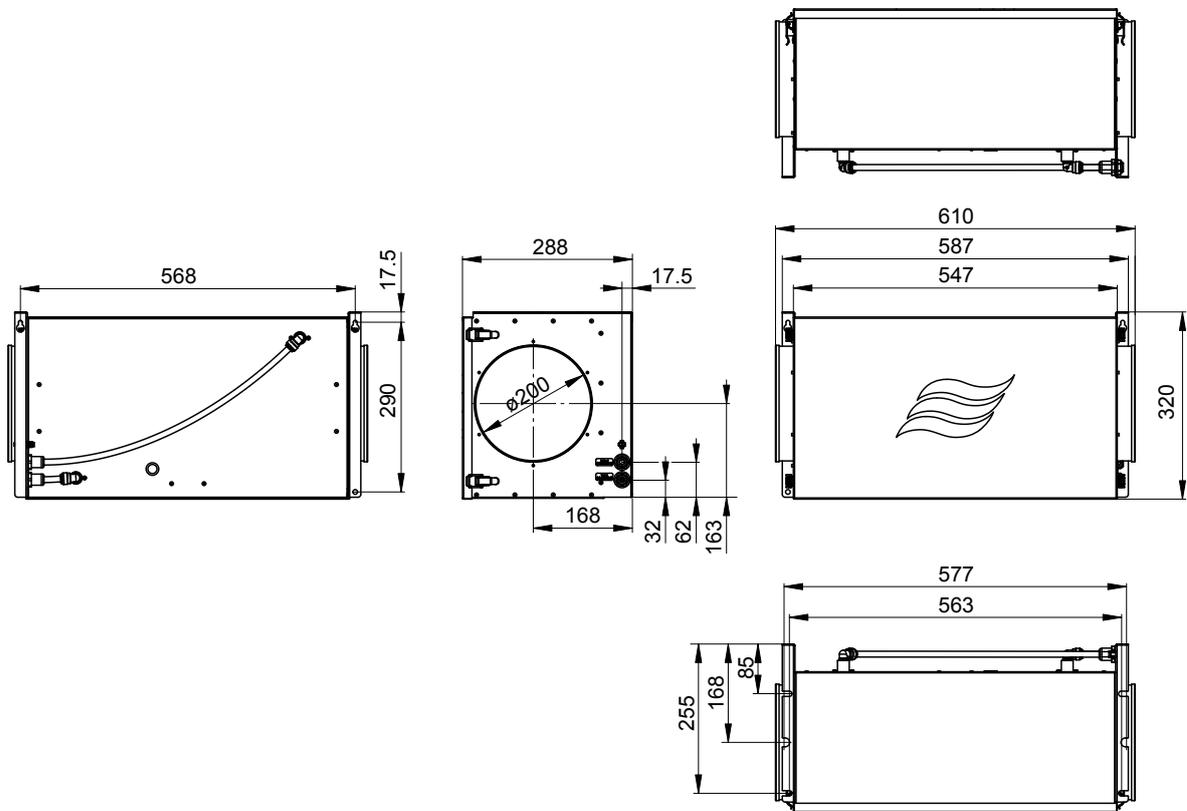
Dimensions unité d'humidification (dimensions en mm)
